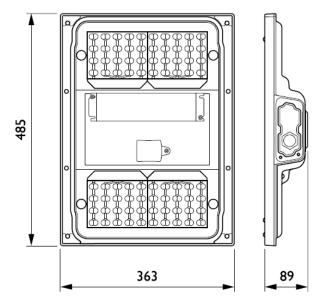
Plano módulo luminaria. Fuente: Catálogo del fabricante
